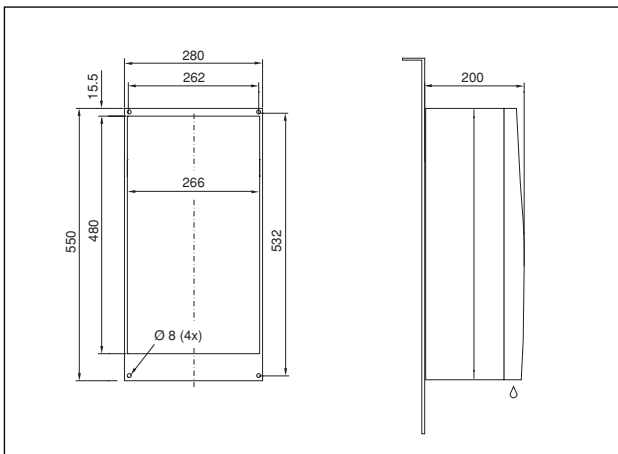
SK 3303.xxx, SK 3361.xxx Påbyggnad
